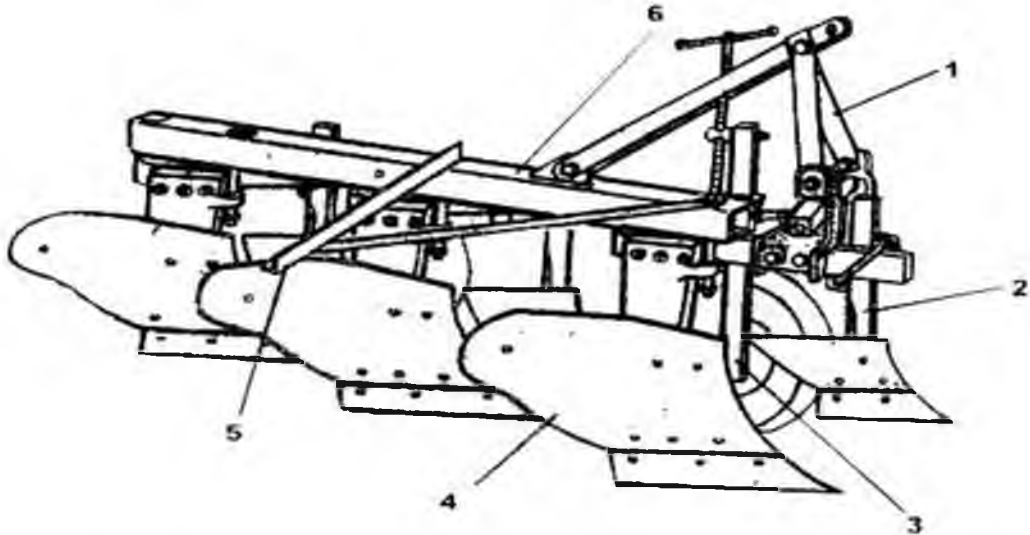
Грунтообробного робочого органу трьохкорпусний навісний ПЛН 3-35; 1 - причіпний механізм; 2 - передплужник; 3 - опорне колесо; 4 - корпус плуга; 5 - причеплення для борни; 6 - рама
